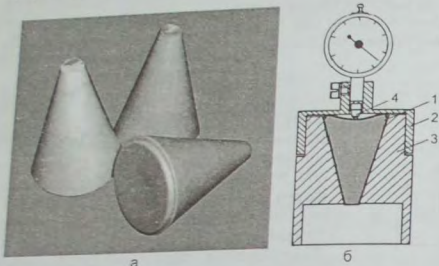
Общий вид образцов (а) и схема проведения замера глубины утяжины в образце (б)
